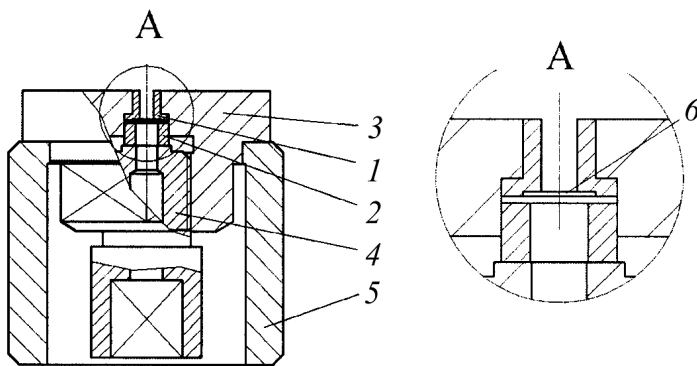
Затискний пристрій для фіксації дискового мікрозразка на координатному столику: 1, 2 – верхня та нижня втулки; 3 – обойма; 4 – затискна гайка; 5 – циліндричний стакан; 6 – дисковий мікрозразок.
